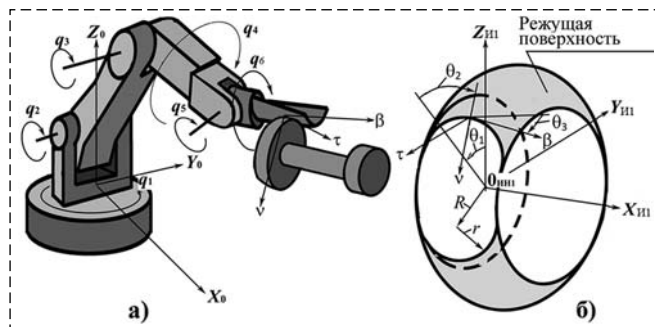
Промышленный робот и представление режущей поверхности инструмента:
